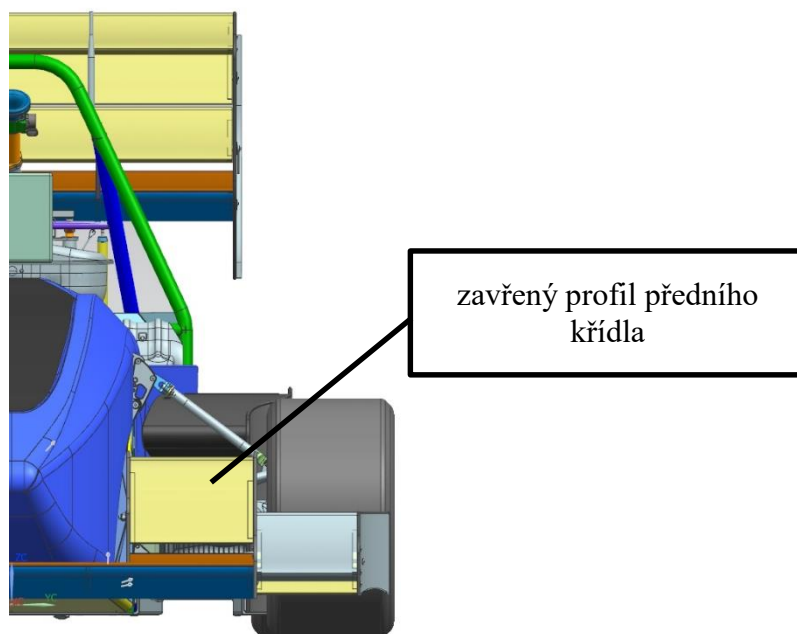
Umístění chladiče v zástavbovém prostoru - boční pohled
